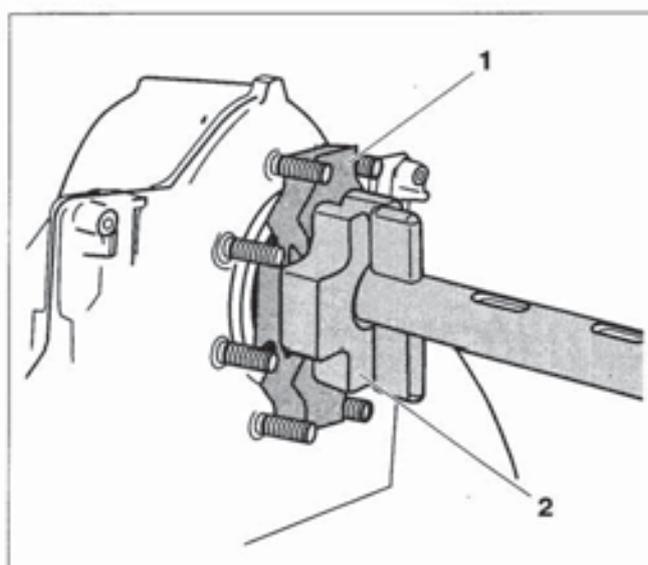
Beispiel: GE615 – Gegenflansch und Zusatzflansch
